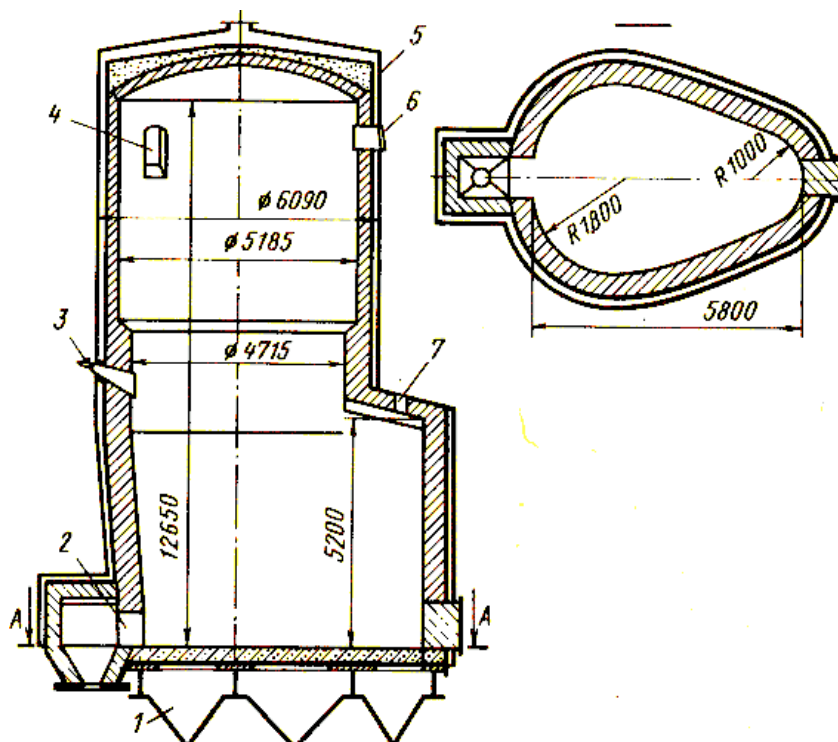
Печь КС, ОАО «Комбинат Южуралникель»: 1 – дутьевая камера; 2 – разгрузочное отверстие; 3 – форсунка для разогрева печи; 4 – газоходное отверстие; 5 – экранирующий кожух; 6 – взрывной клапан; 7 – загрузочное отверстие
